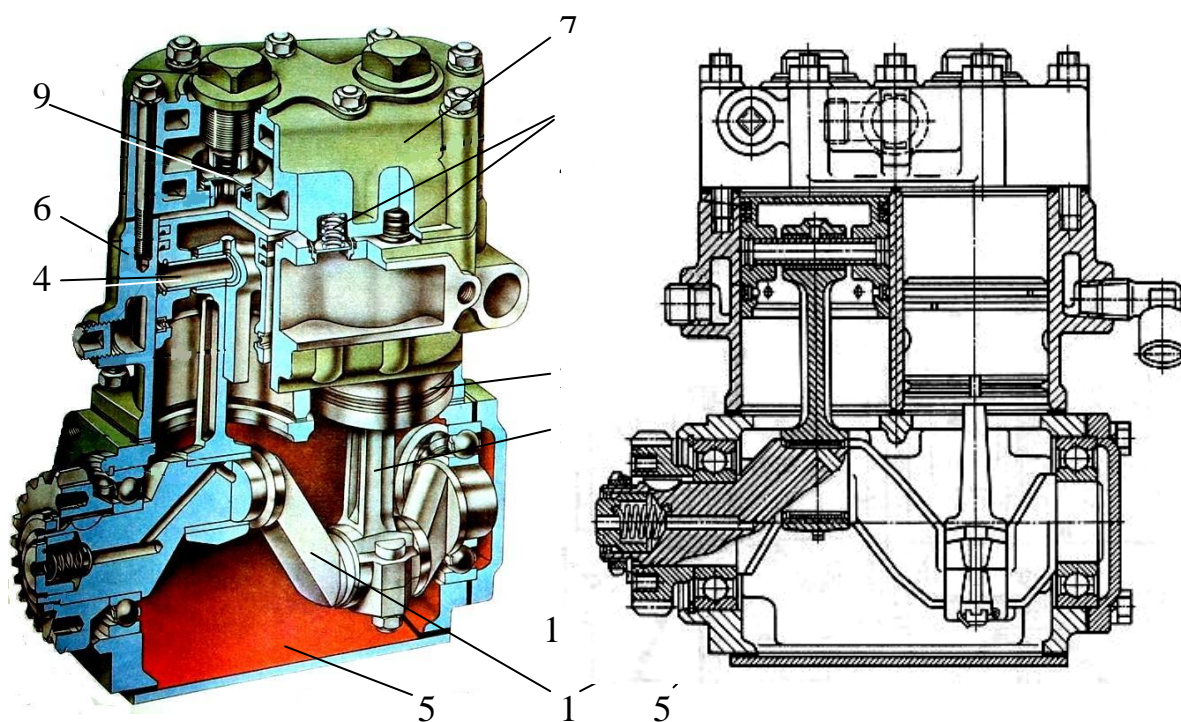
Компрессор грузового автомобиля-тягача КАМАЗ-5320: 1 – коленчатый вал; 2 – поршень; 3 – шатун; 4 – поршневой палец; 5 – картер; 6 – блок цилиндров; 7 – головка блока цилиндров; 8 – впускные клапаны; 9 – выпускной клапан; 10 – штуцер подвода охлаждающей жидкости; 11 – шестерня привода
